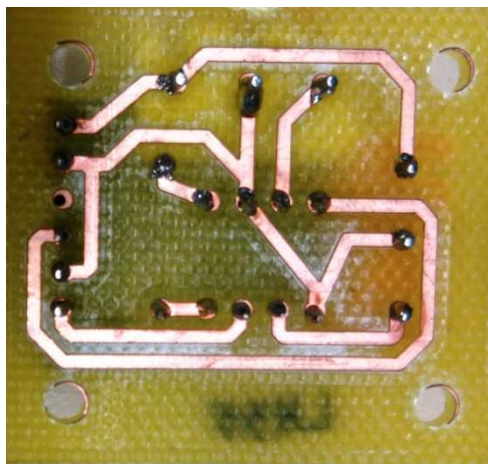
PARTE IMPRESA DE LA PCB DEL MÓDULO PARA EL SENSADO MEDIANTE LM35
